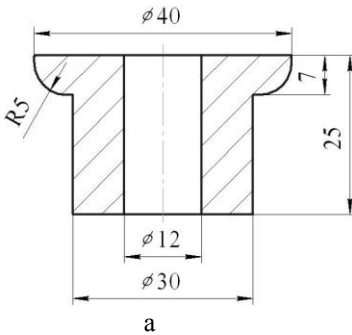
Заготовка деталі «втулка з буртом» після штампування:
